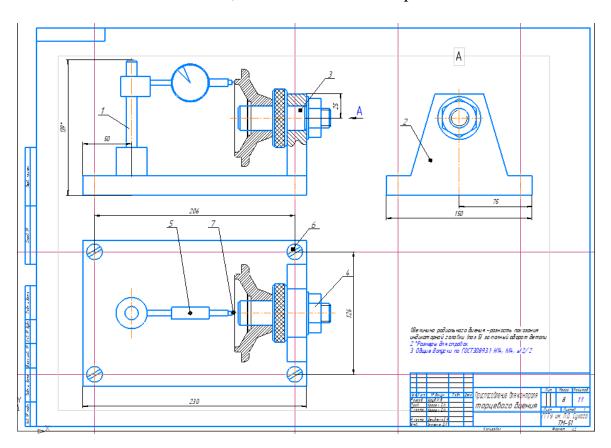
Чертеж приспособления для контроля торцевого биения
